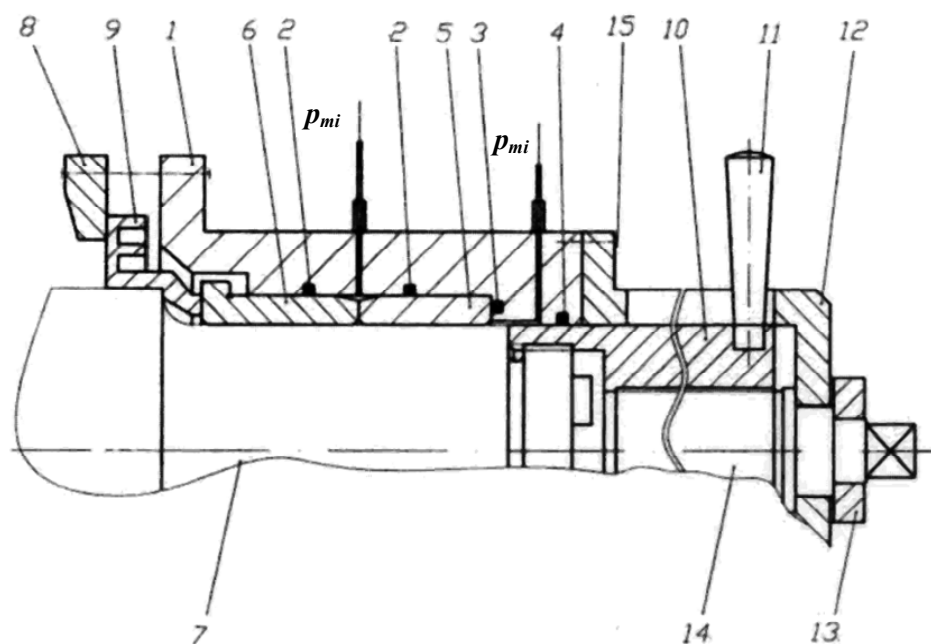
Принципиальная схема устройства для распрессовки колец буксовых подшипников и кольца лабиринтного уплотнения буксы колесной пары:
